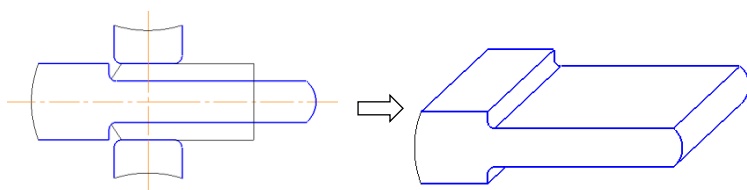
Схема получения двустороннего уступа для призматических заготовок
